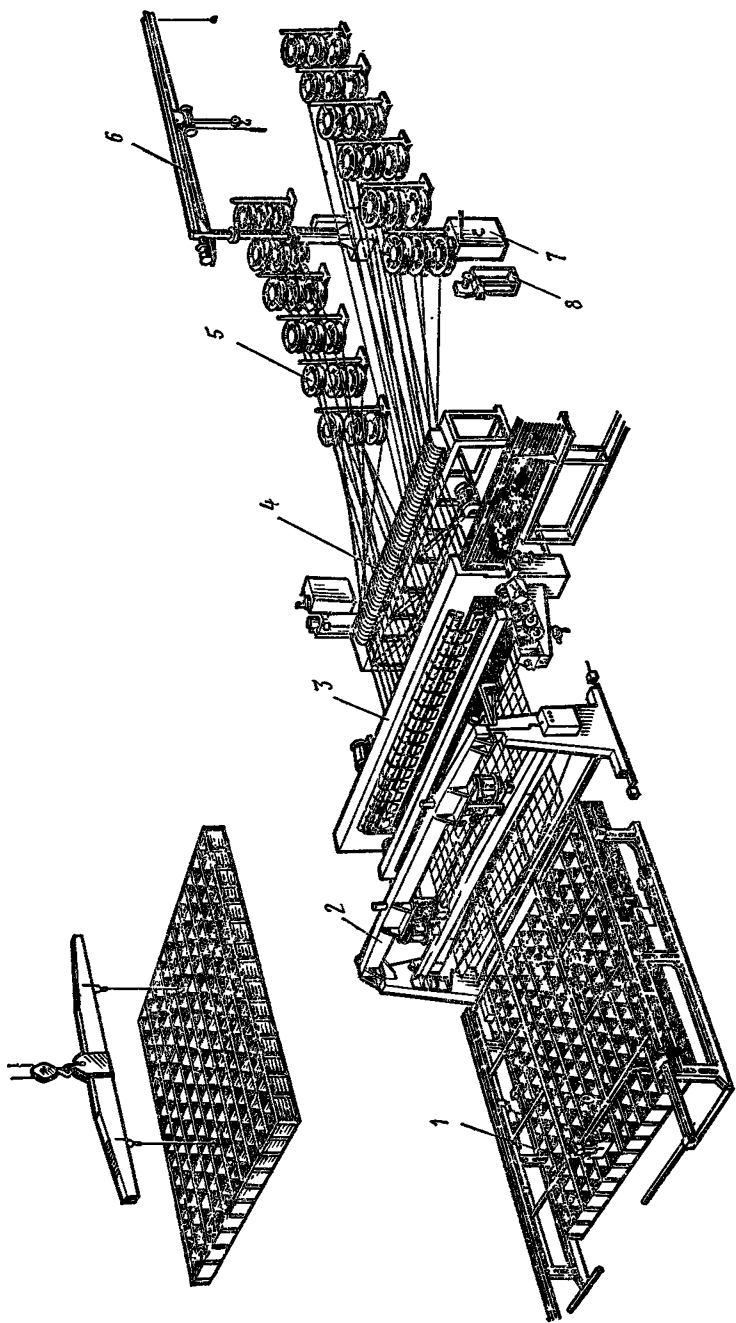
Линия 2880-1 на базе сварочной машины АТМС 14×75-7-1 для изготовления armатурных секгов:
